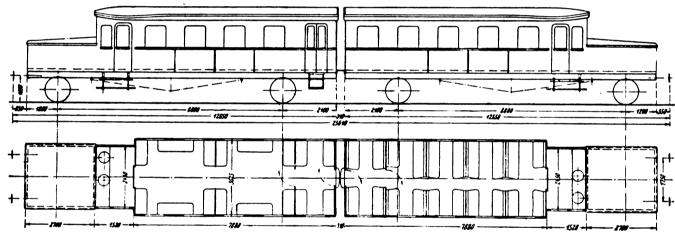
e 11. - Automotrici ad accumulatori, delle Perrovie di Stato Prussiane - Elevazione e pianta.
